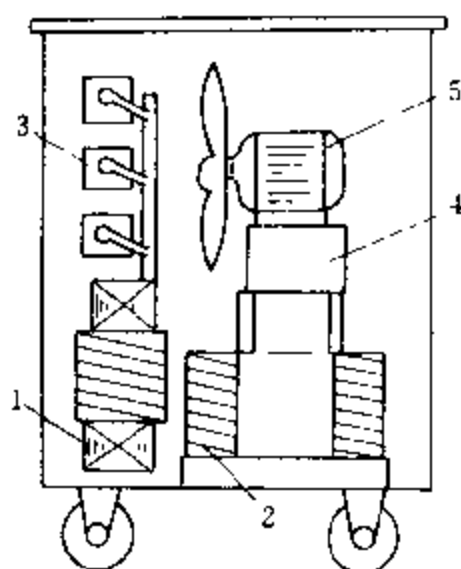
ZXG-300 型硅整流弧焊机结构示意图
